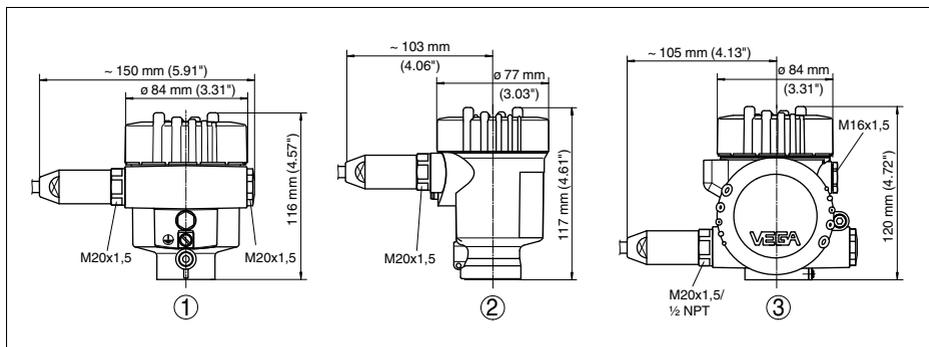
Корпуса в исполнении IP 66/IP 68 (1 bar) - с установленным модулем индикации и настройки корпус выше на 9 mm/0.35 in
